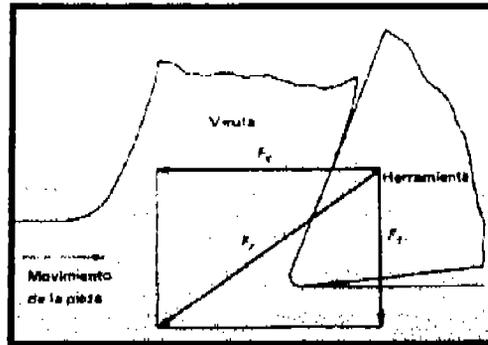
Fuerzas que actúan sobre la herramienta de corte. (Fundamentos del corte de metales y de las máquinas herramientas).
